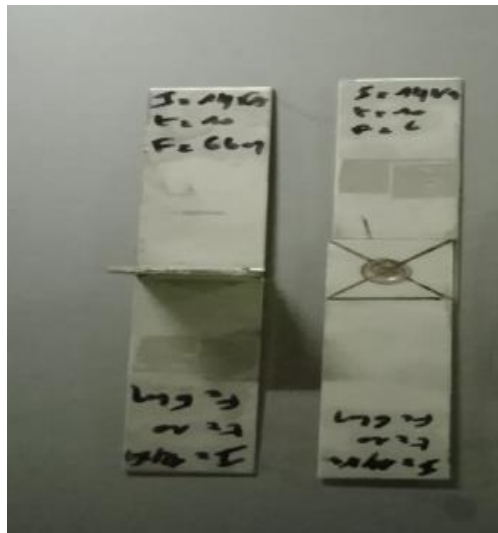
Joints par recouvrement et Peel-joints après le soudage.
